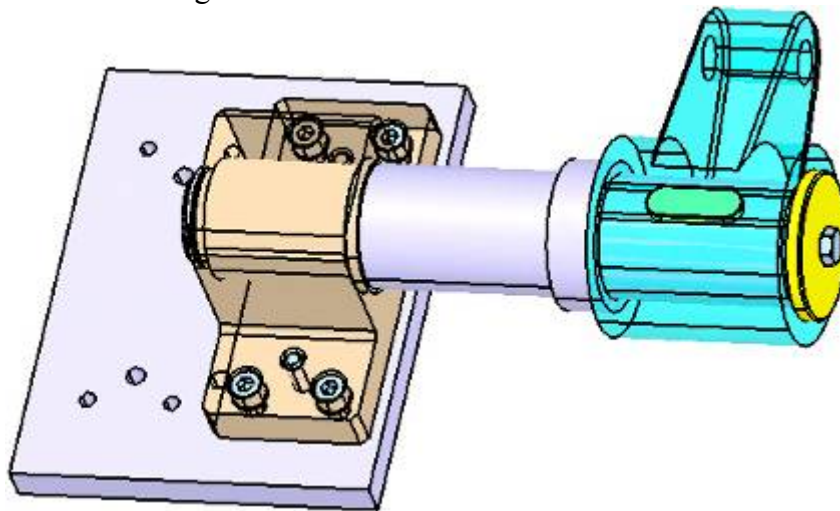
Asamblarea arborelui cu suportul prin intermediul lagărului
